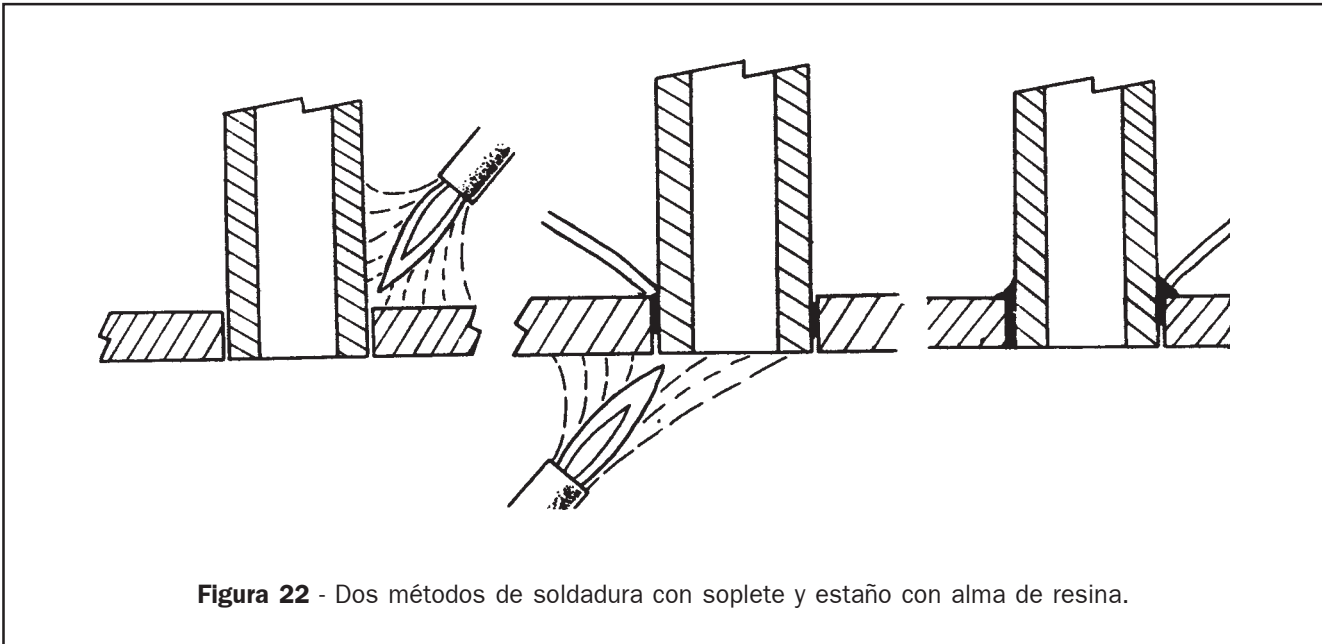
Dos métodos de soldadura con soplete y estaño con alma de resina.
